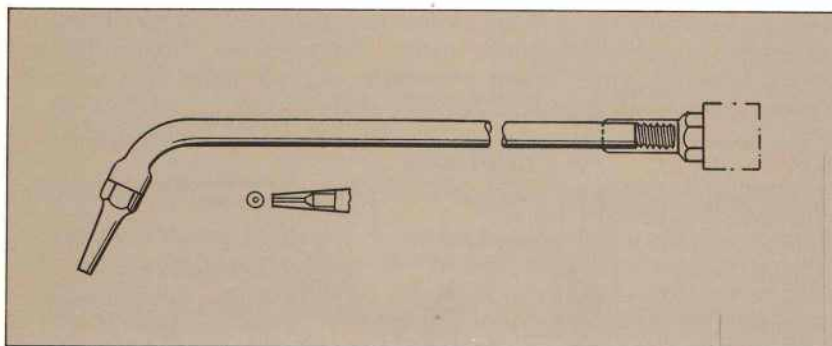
Soplete de oxiacetileno utilizado en la soldadura dura.
